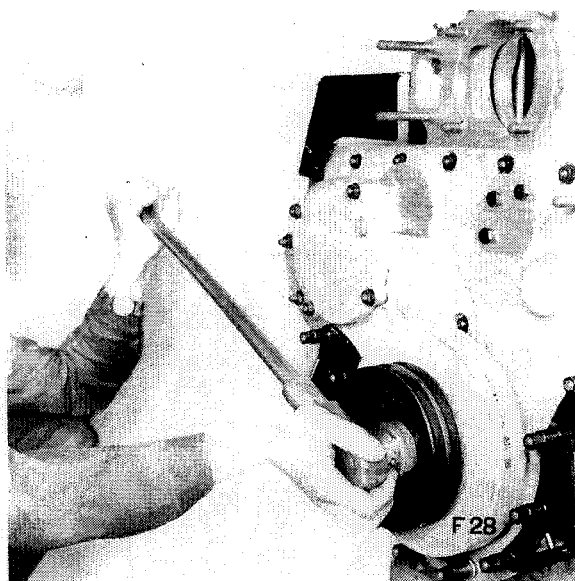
Lösen der Sechskantschraube im Zentrum der Kurbelwelle
